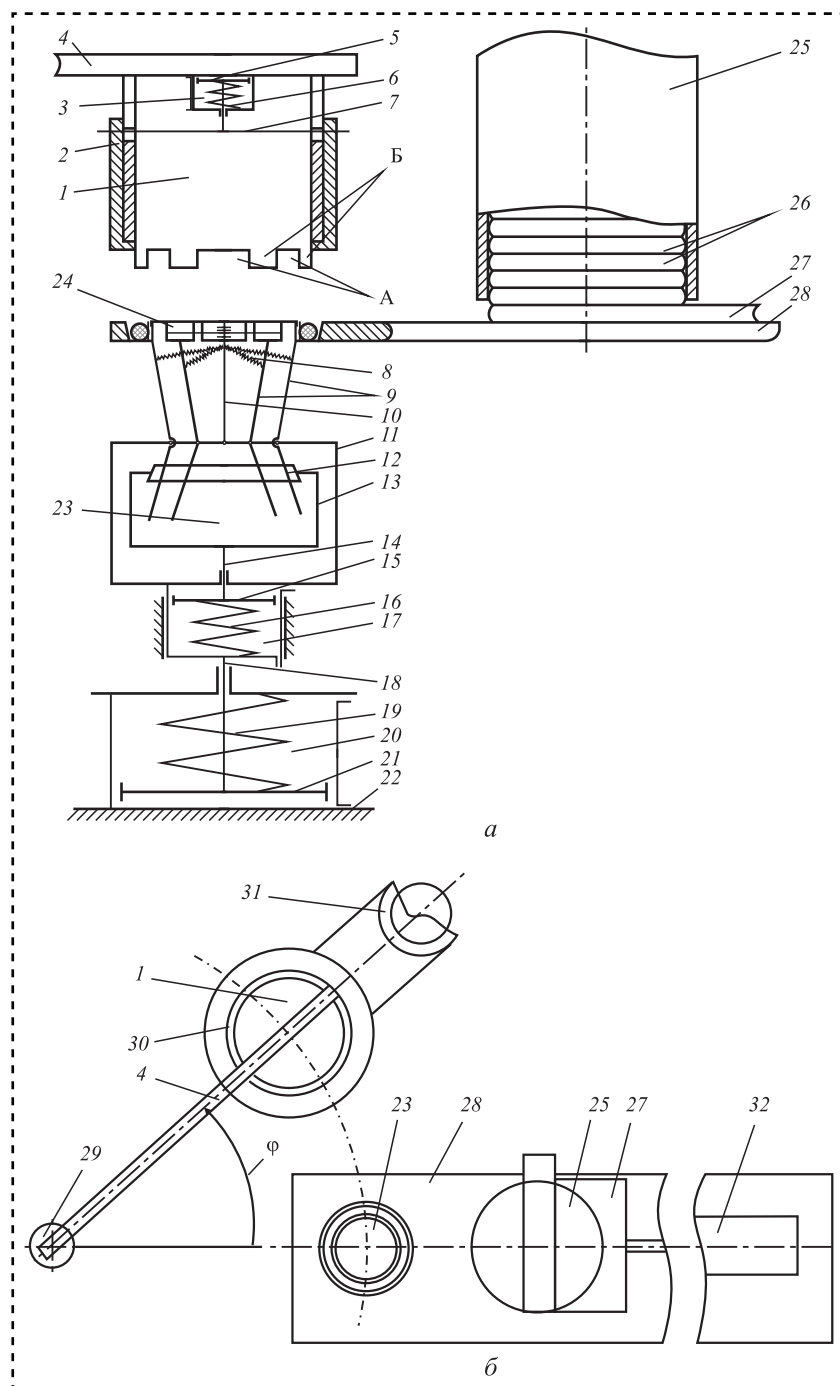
Кинематическая схема (а) и вид сверху (б) устройства для установки упругих колец в наружные канавки цилиндрических деталей
